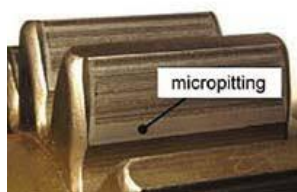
Desgaste por *micropitting* em engrenagens [6]
